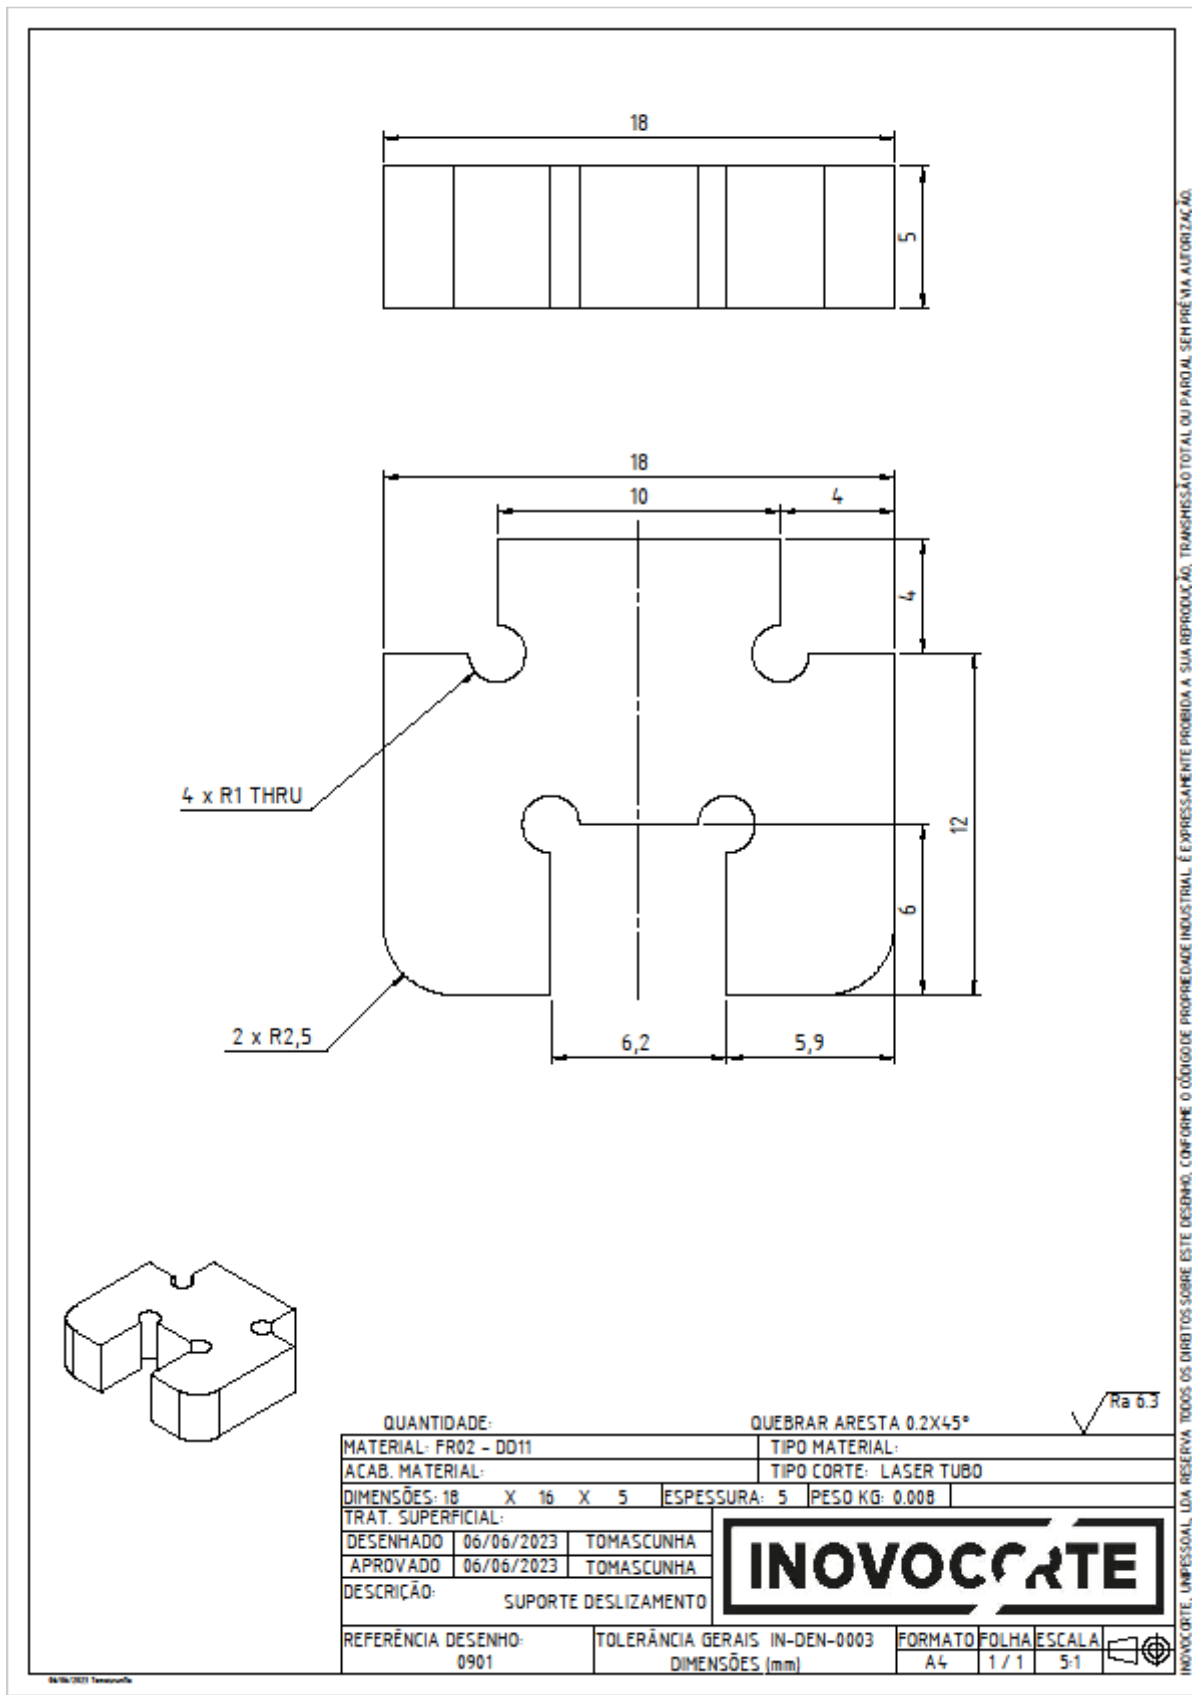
Desenho técnico do suporte deslizamento (0901).
